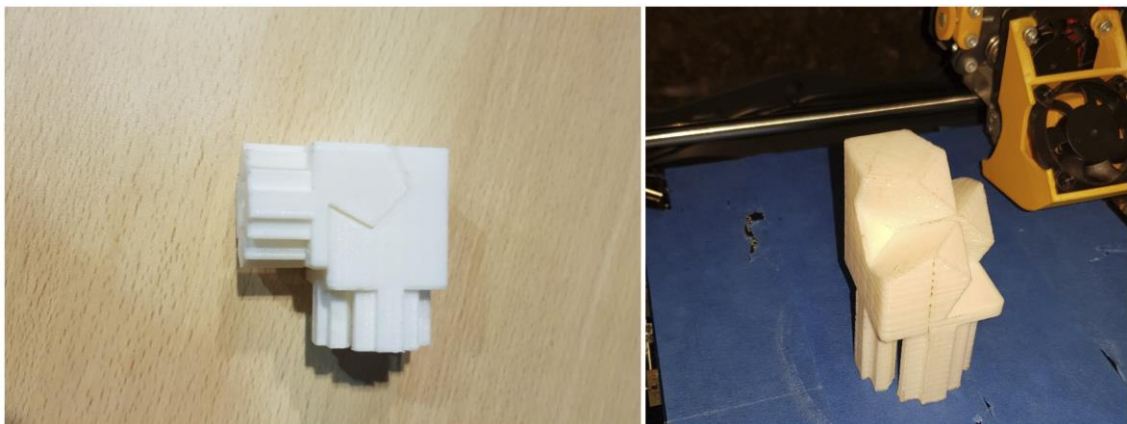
Imagens referentes à impressão das peças constituintes do sistema de união. Imagem: Jorge Passos
